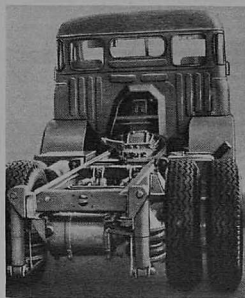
Установка пневматической подвески на шасси грузового автомобиля.
